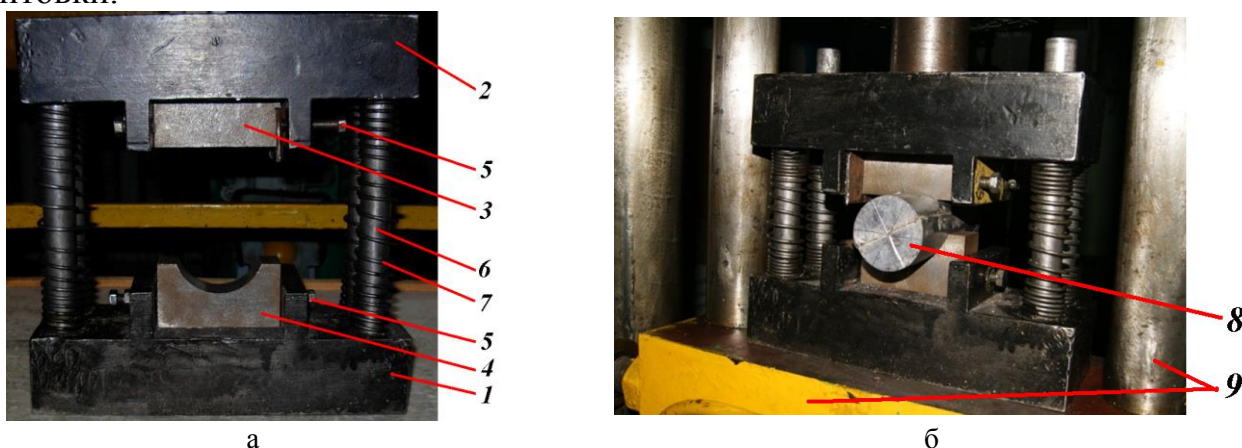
Универсальная испытательная машина: а – штамповый блок для исследования; б –:протяжки заготовок; 1 и 2 – нижняя и верхняя плиты; 3 и 4 – верхний плоский и нижний вырезной бойки; 5 – крепёж; 6 и 7 – направляющие и пружины; 8 – образец; 9 – испытательная машина
